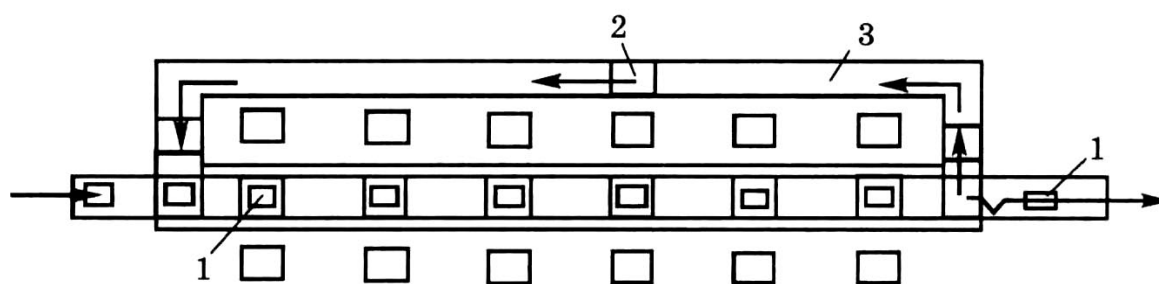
Пример компоновки линии с жесткой связью и приспособлениями-спутниками
